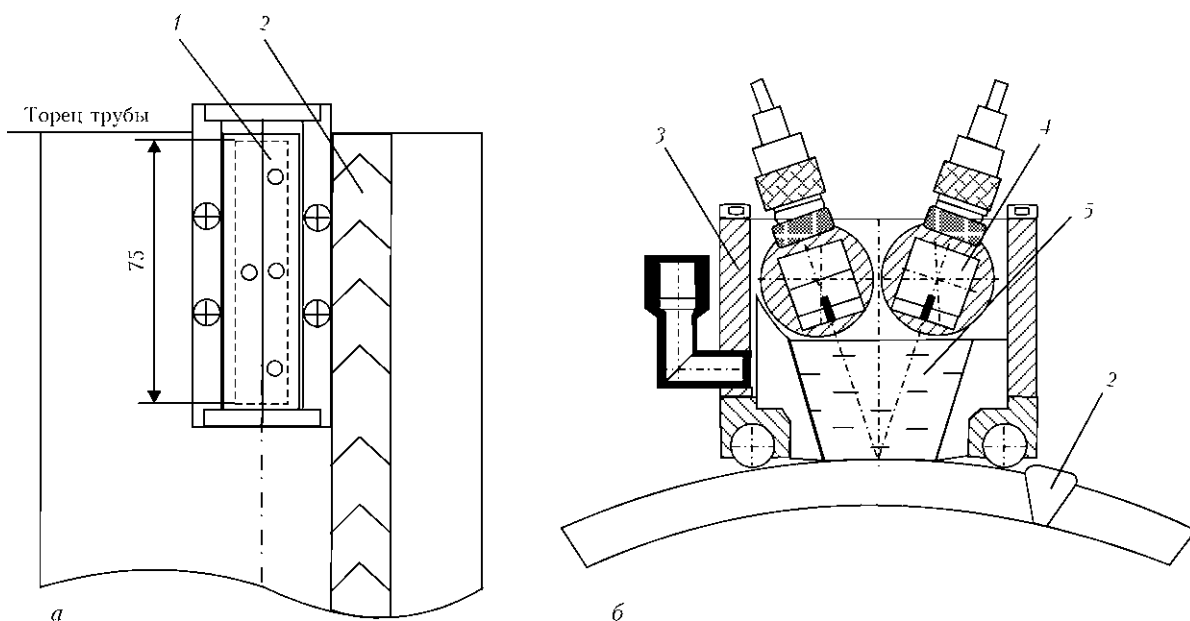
Акустические блоки установки НК 362МХ для контроля на расслоения (а) и на продольные дефекты (б): 1 — акустический блок со специализированным УЗ преобразователем для контроля на расслоения; 2 — сварной шов контролируемой трубы; 3 — локально-иммерсионный акустический блок для контроля на продольные дефекты с десятью УЗ преобразователями (угол ввода ультразвука в металл 45°); 4 — иммерсионный УЗ преобразователь для контроля на продольные дефекты; 5 — локально-иммерсионная ванна (иммерсионная жидкость — вода)
